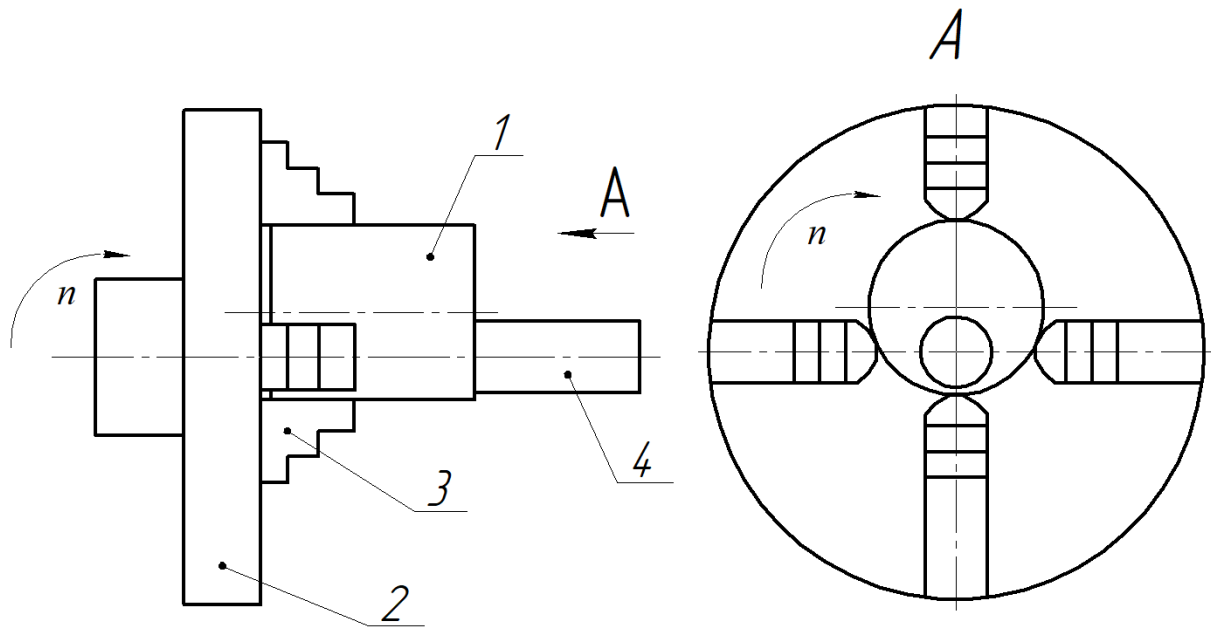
Схема встановлення та затиску заготовки у чотирьохкулачковому патроні: 1 - заготовка; 2 - патрон, 3 - кулачки, 4 -ексцентрикова поверхня
